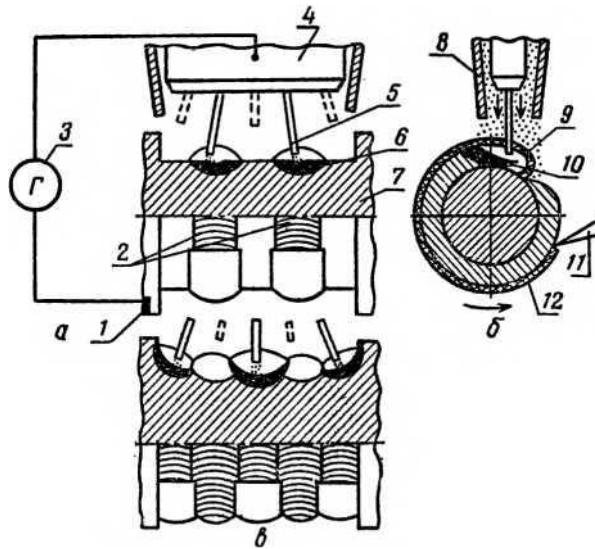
Схема багатоелектродного наплавлення в окремій зварювальній ванні:
